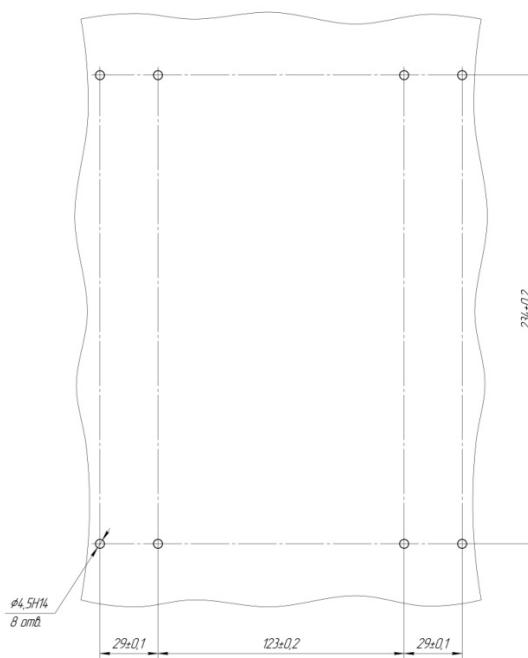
Габаритные и присоединительные размеры устройства PC830-M1 при внешнем монтаже, обеспечивающем его поворот вверх/вниз
